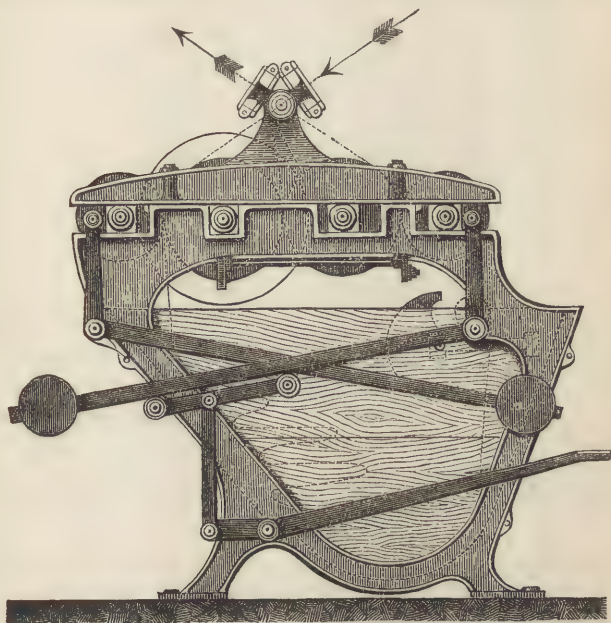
Chlor-Kalk- und Säuremaschine. (Haubold.) Seitenansicht.
